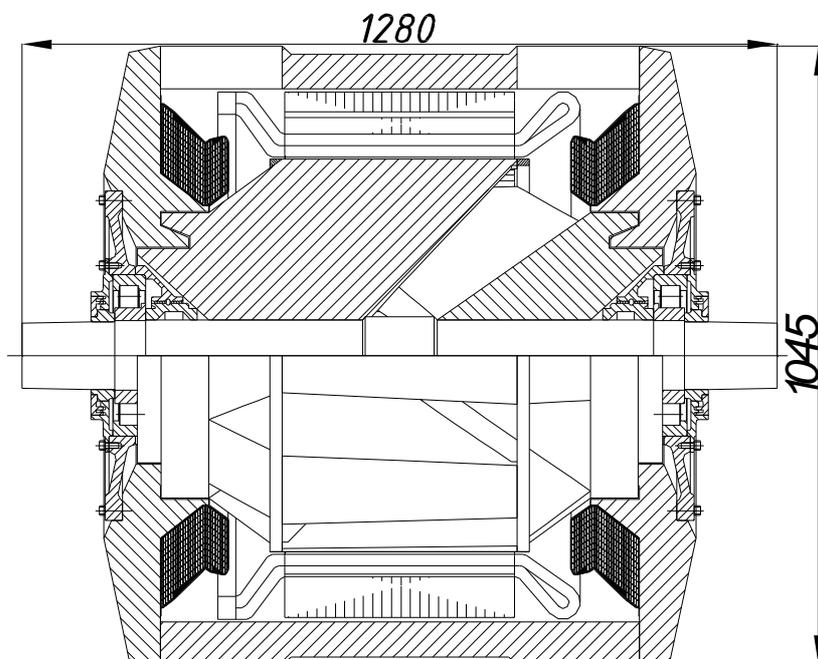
Продольный разрез вентильного двигателя с когтеобразными полюсами
